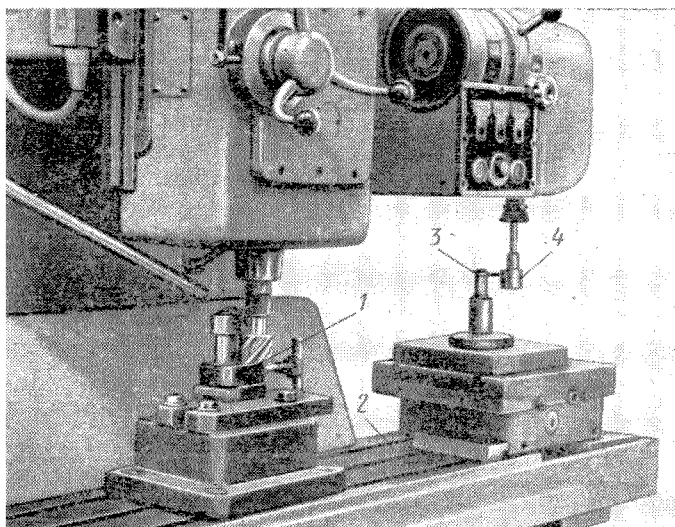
Схема обработки наружных профилей лопаток на копировально-фрезерном станке 642К
